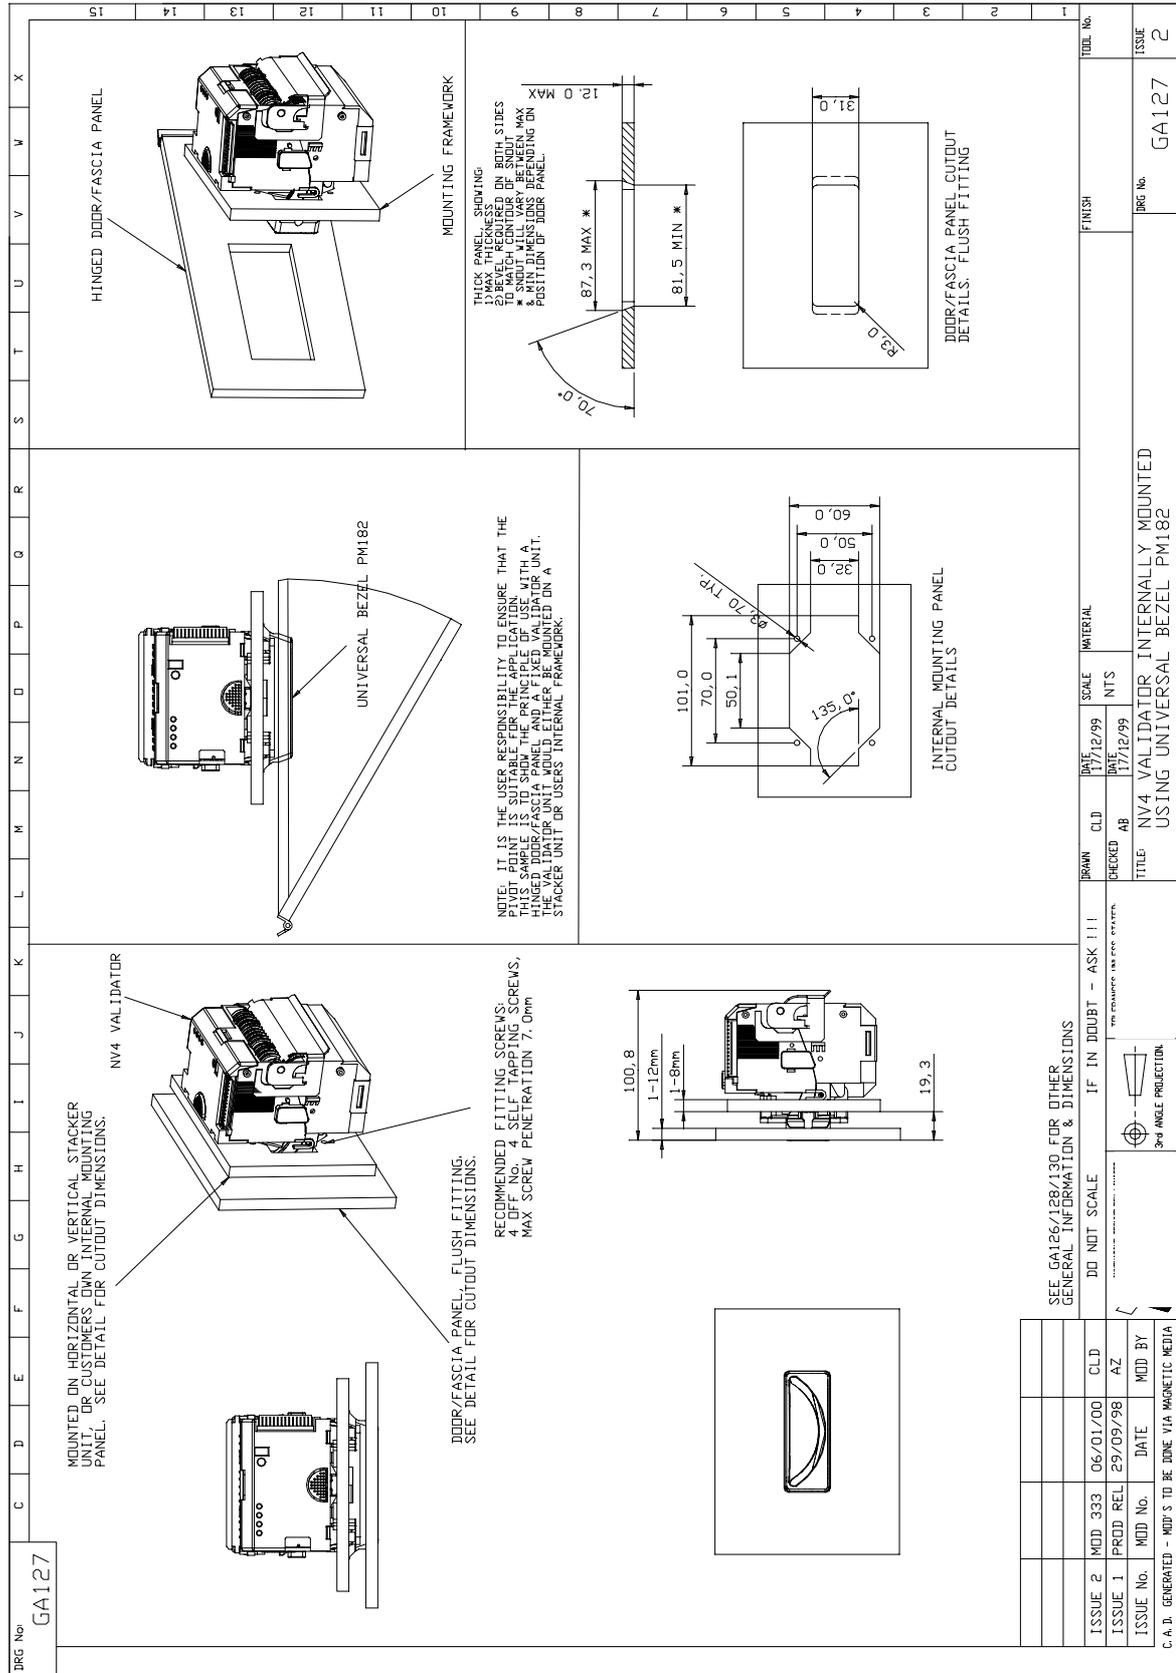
NV4 Einbau im Automatengehäuse / intern mit Universal Frontblende
